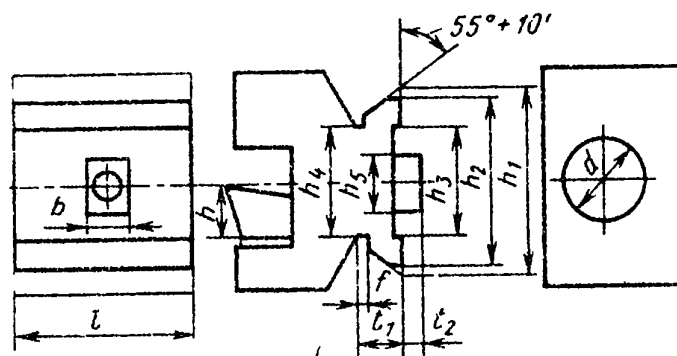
Варианты исполнения резцедержателей с базирующей призмой
